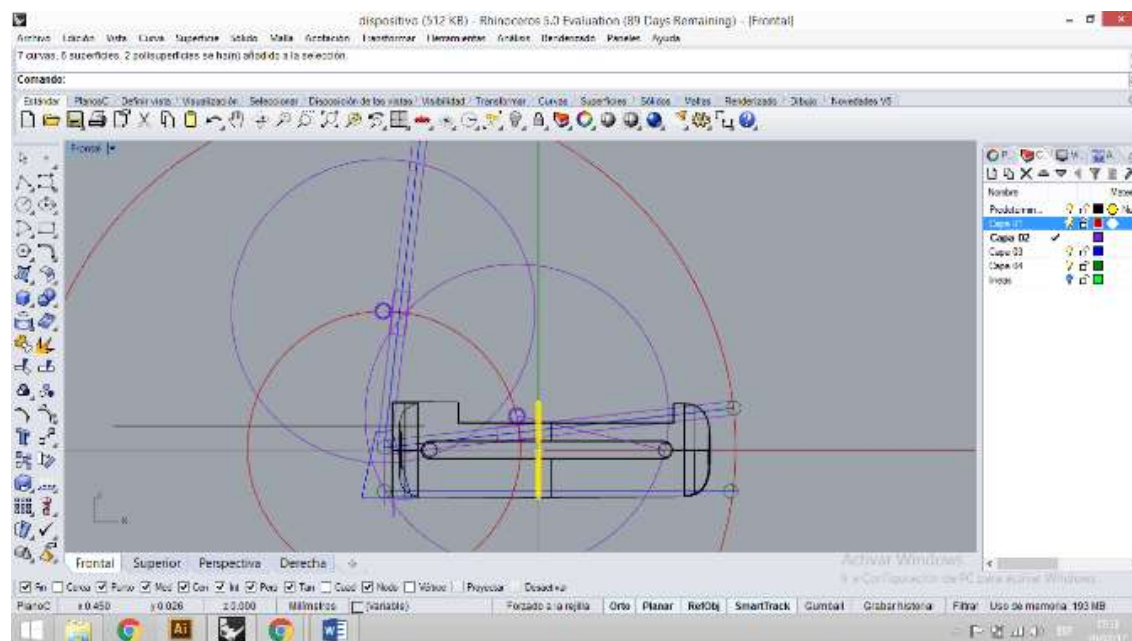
DISEÑO EN AUTOCAD TRABAJO DE PLANIMETRÍA
